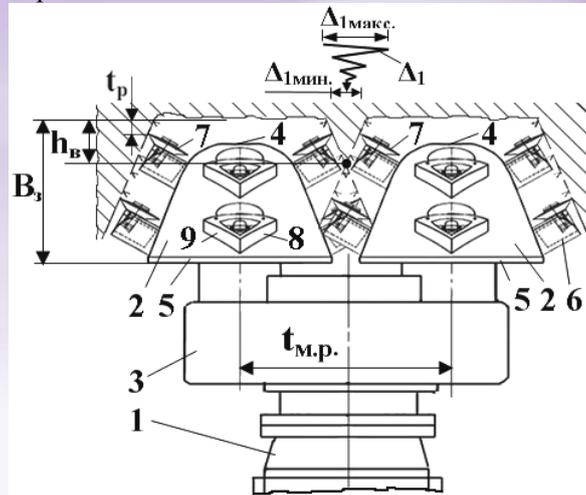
Двухкорончатый исполнительный орган реверсивного действия
